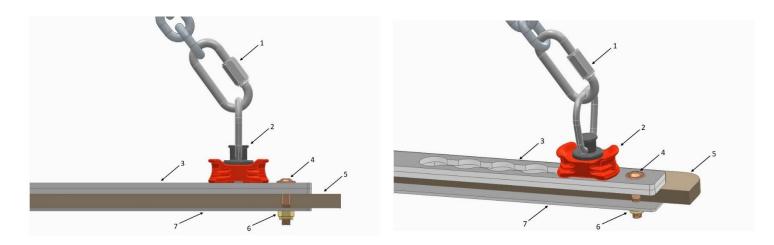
Схема установки такелажных колец. 1 – карабин; 2 – быстросъемный фитинг; 3 – планка напольного покрытия; 4 – крепежный винт М6; 5 – напольное покрытие; 6 – гайка М6; 7 – планка – шайба.
